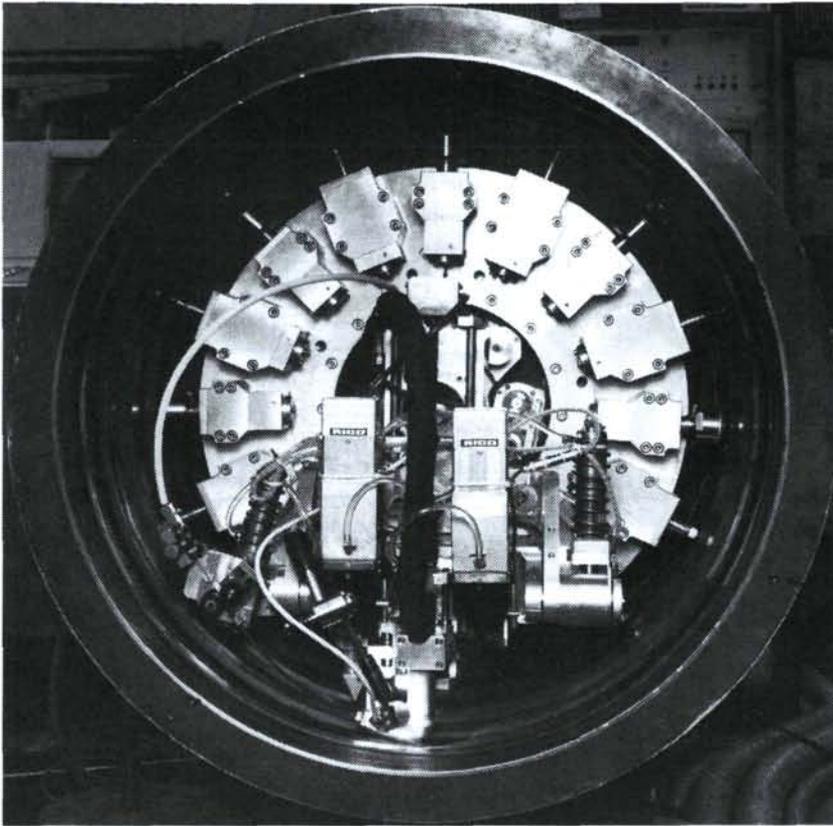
Máquina de soldar para el revestimiento interno de tuberías.
